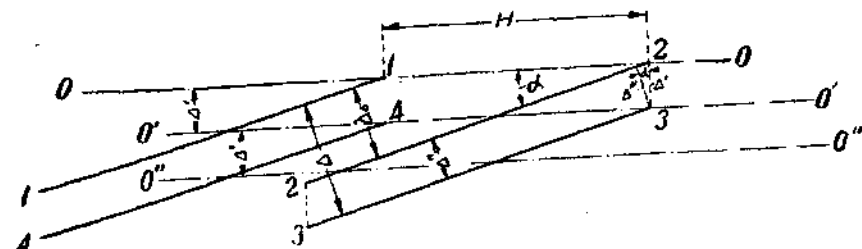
Схема расположения пилы станка «Лисий хвост».
